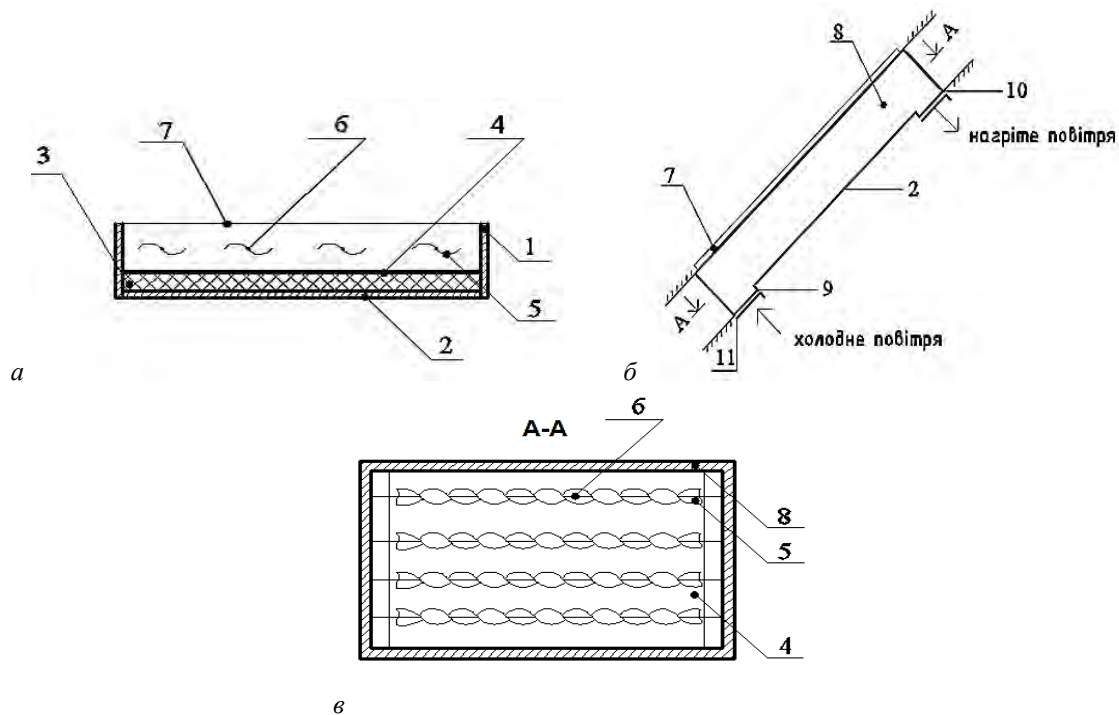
а – сонячний колектор в розрізі; б – встановлений на даху сонячний колектор; в – розріз по А-А; 1 – бокова стінка корпусу; 2 – дно корпусу; 3 – шар теплоізоляційного матеріалу; 4 – теплопоглинальна пластина; 5 – турбулізатор потоку; 6 – металевий стрижень; 7 – світлопроникна пластина; 8 – корпус; 9 – вхідний отвір; 10 – вихідний отвір; 11 – регулювальна заслінка
